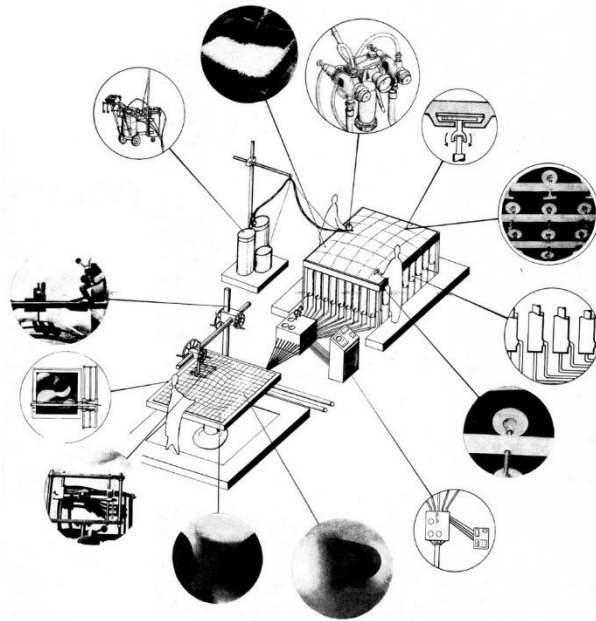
Diseño del molde flexible diseñado por Renzo Piano.
